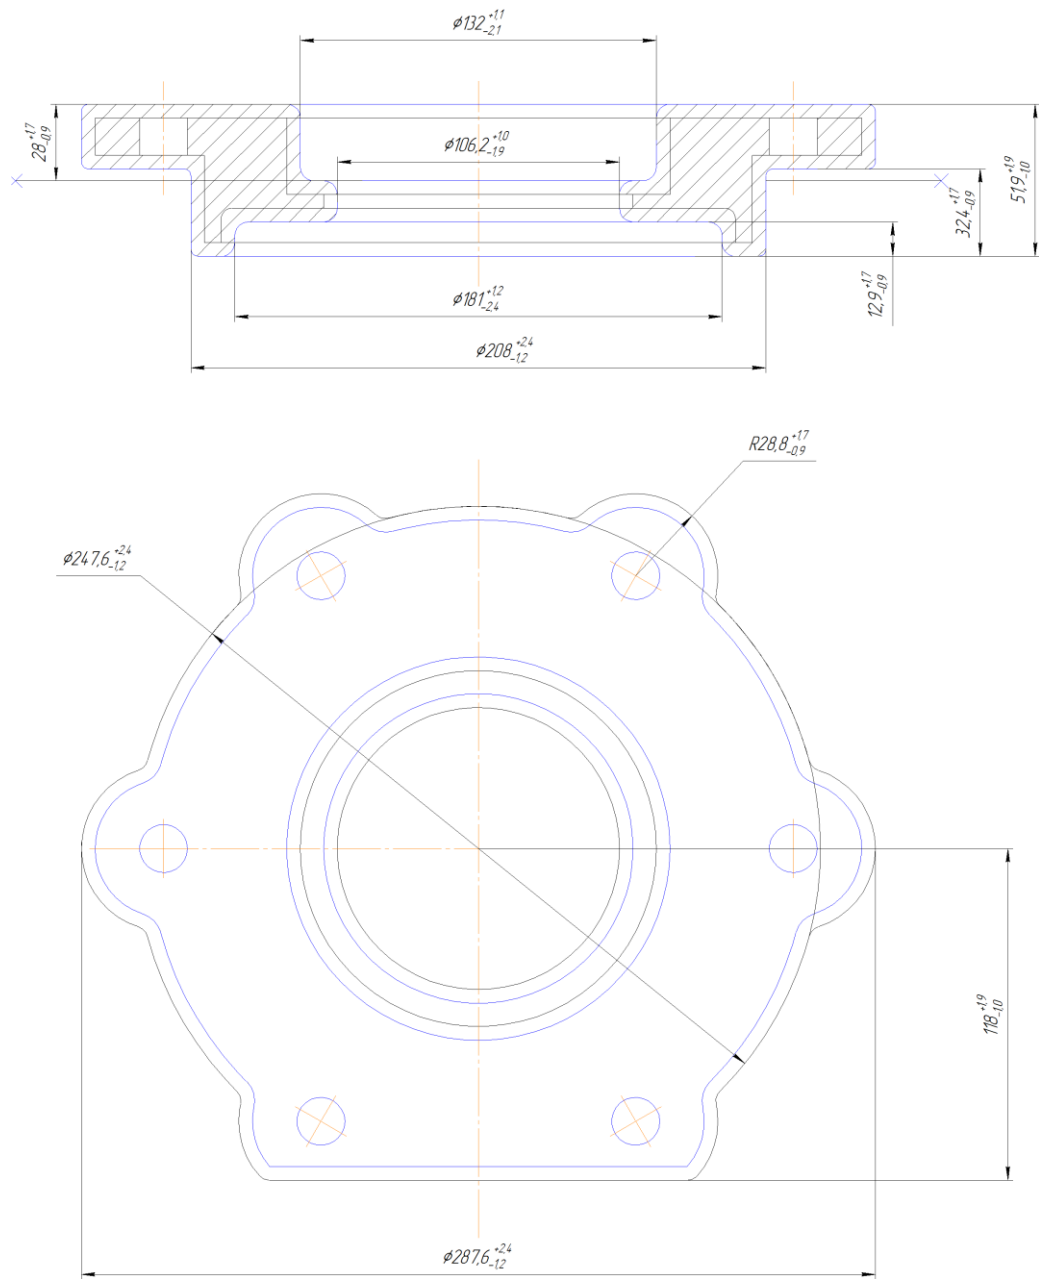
Заготовка кришки наскрізної БР.ПМЗ-19-275.00.001 отримана методом гарячої об'ємної штамповки.
